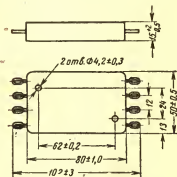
Габаритный чертеж столбов КЦ401Б.
